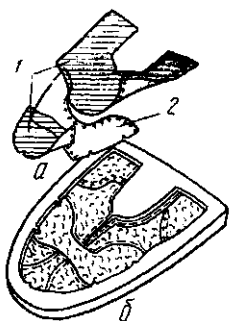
Детали заготовки с гидрофильными вставками (а) и силиконовая матрица (б):
